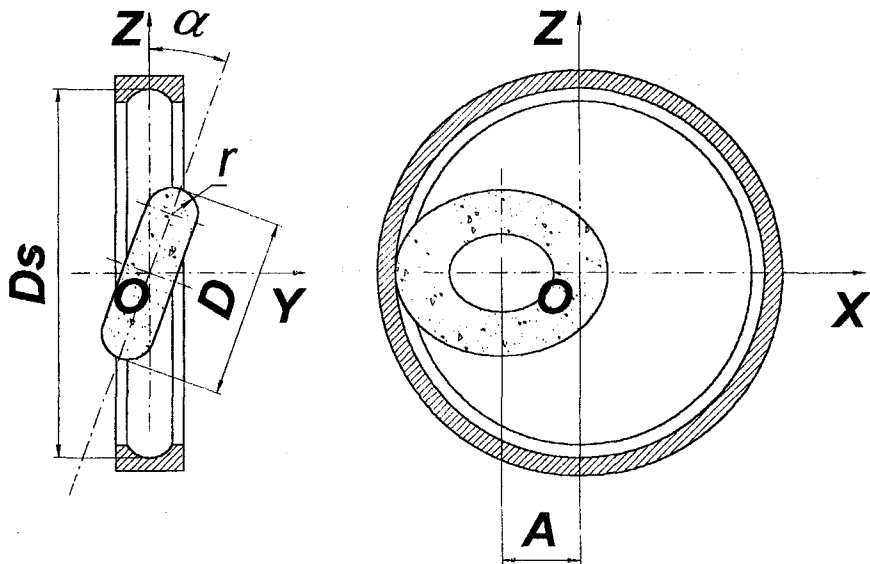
Схема способа шлифования наклонным кругом деталей типа наружных колец подшипников
